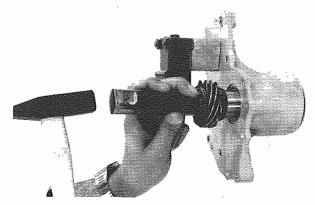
Ingranaggio comando spinterogeno Distributor control gear
